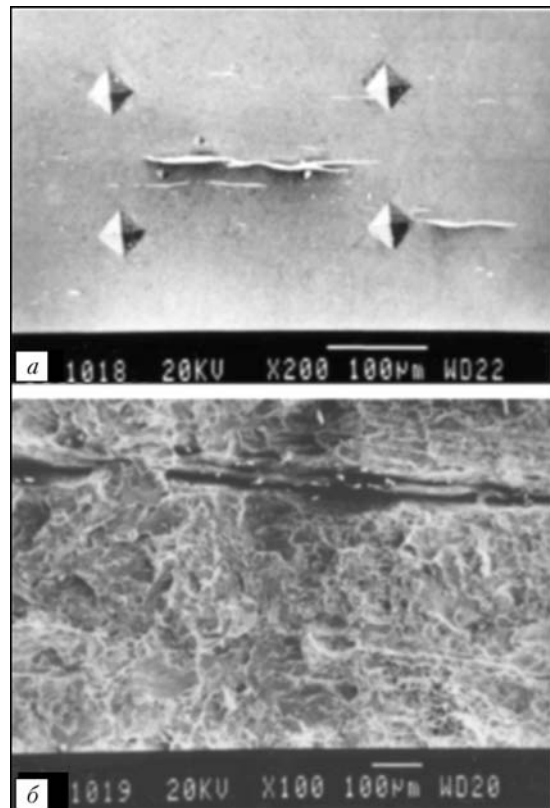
Крупные включения в корпусе абсорбера из стали 20К: а — поверхность шлифа; б — поверхность излома
